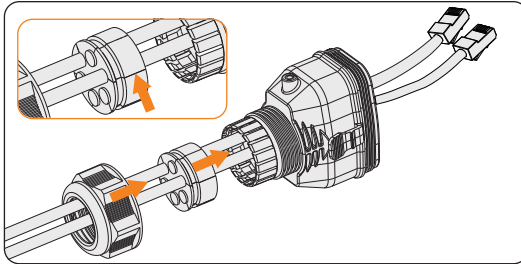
Kabel mit RJ45-Klemme einfädeln
